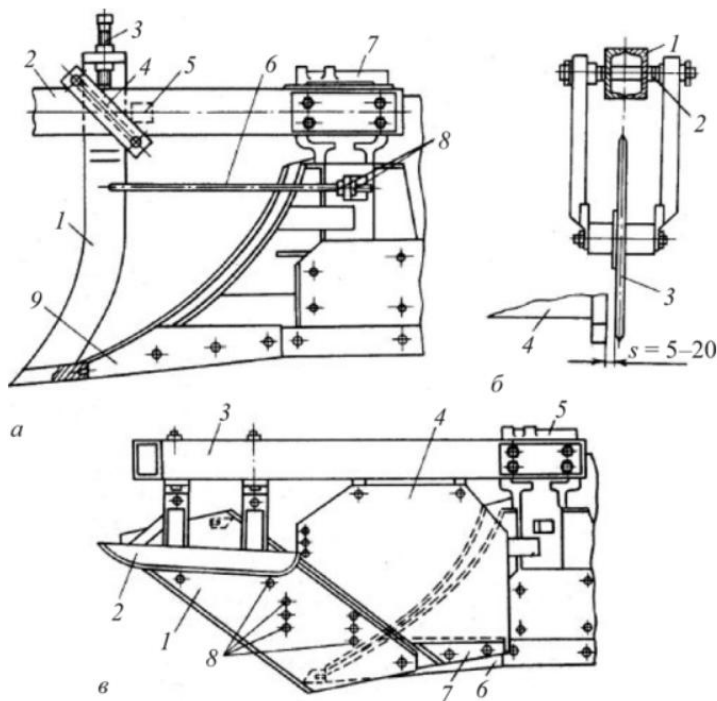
Установка и регулировка ножей: а — черенкового: 1 — черенковый нож-резец; 2 — рама плуга; 3 — болт; 4 — планка; 5 — кронштейн; б — натяжной прут; 7 — стойка корпуса плуга; 8 — гайки; 9 —
